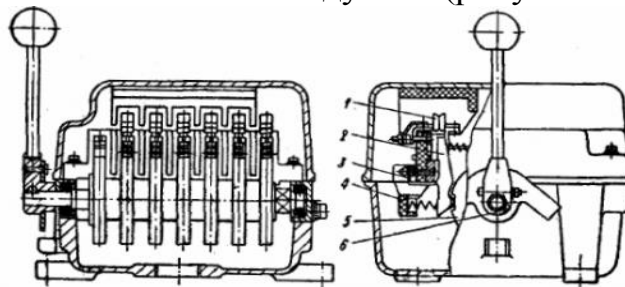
Кулачковый контроллер ККТ60А: 1- главные контакты; 2- рычаг; 3- пластмассовая рейка; 4- гибкое соединение; 5- кулачковые шайбы; 6-рукоятка
